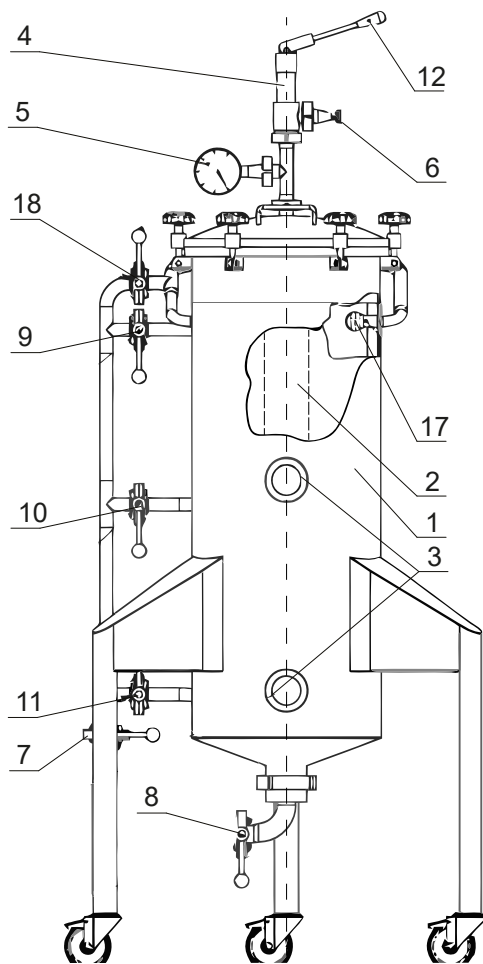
Общий вид устройства для сухого охмеления:
